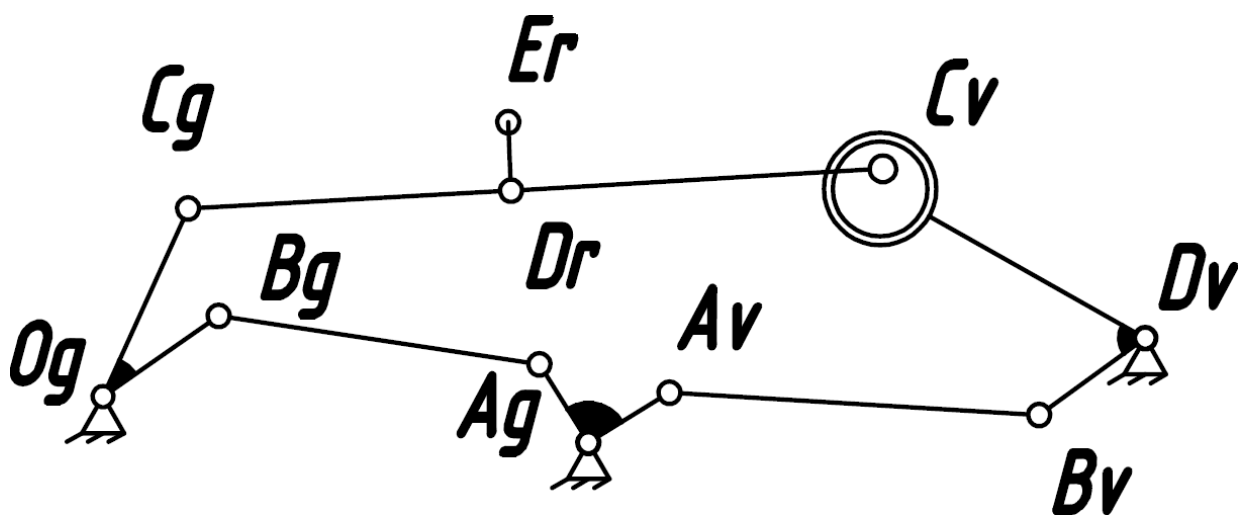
Розрахункова схема механізму зубчастої рейки швейної машини 1022М кл.
